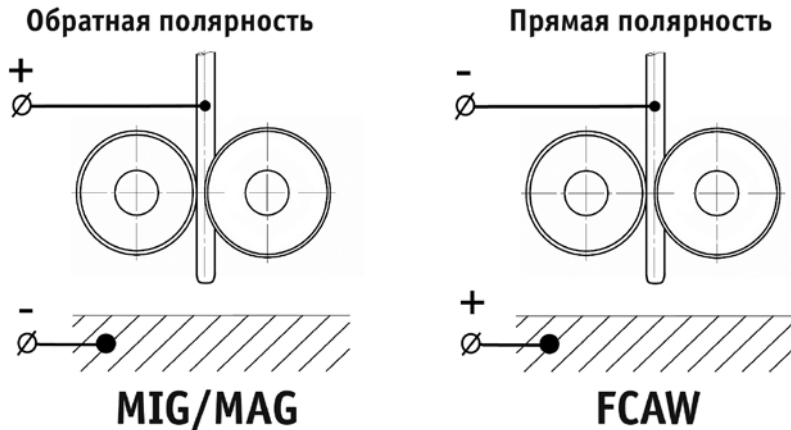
Выбор полярности при MIG/MAG и FCAW сварке.
